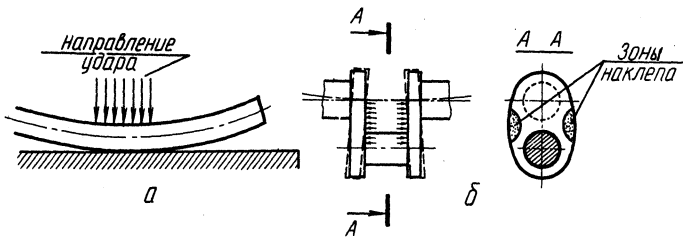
Правка наклепом: а — прямой вал; б — коленчатый вал
